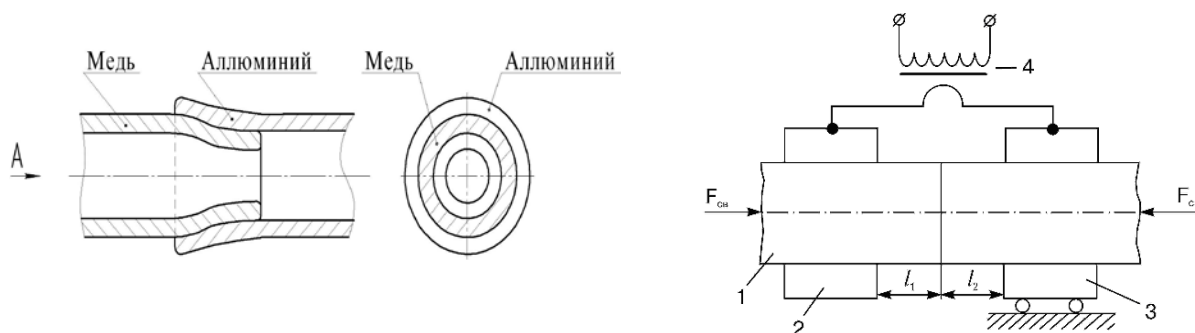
а – телескопическое сварное соединение Cu-Al трубок, б - схема контактной стыковой сварки: 1 – свариваемые детали; 2 – неподвижный зажим; 3 – подвижный зажим; 4 – сварочный трансформатор;  $F_{сж}$  – сжимающее усилие;  $l_1$  и  $l_2$  – нагреваемые вылеты деталей
